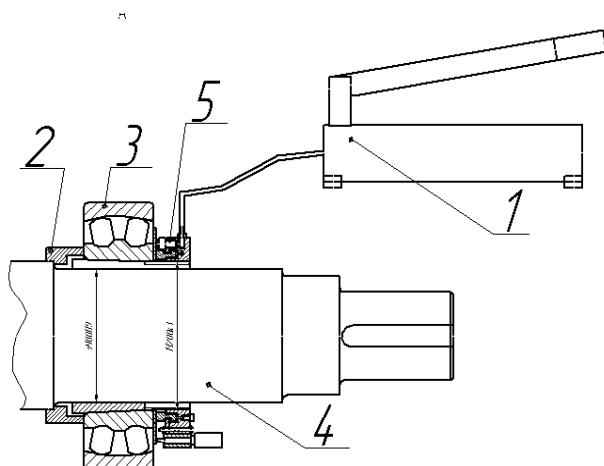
Использование гидрогайки: 1 – насос; 2 – упорная втулка; 3 – подшипник; 4 – цапфа вала; 5 – гидравлическая гайка
